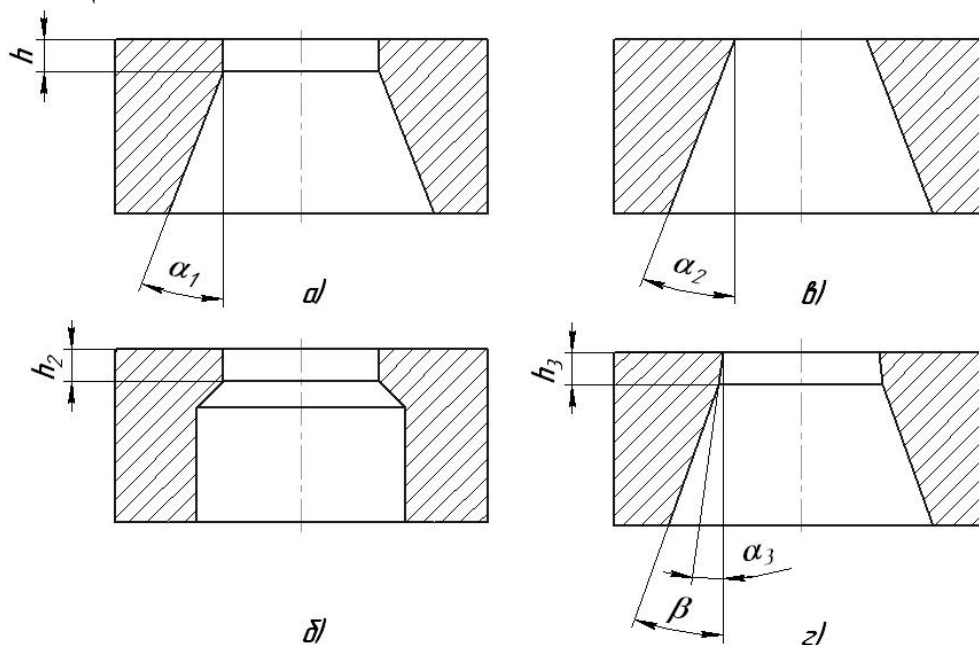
Профіль робочої частини матриці: а – з циліндричним пояском; б – з двома циліндричними ділянками; в – з конусом від робочої (дзеркальної) поверхні; г – з двома конусами
